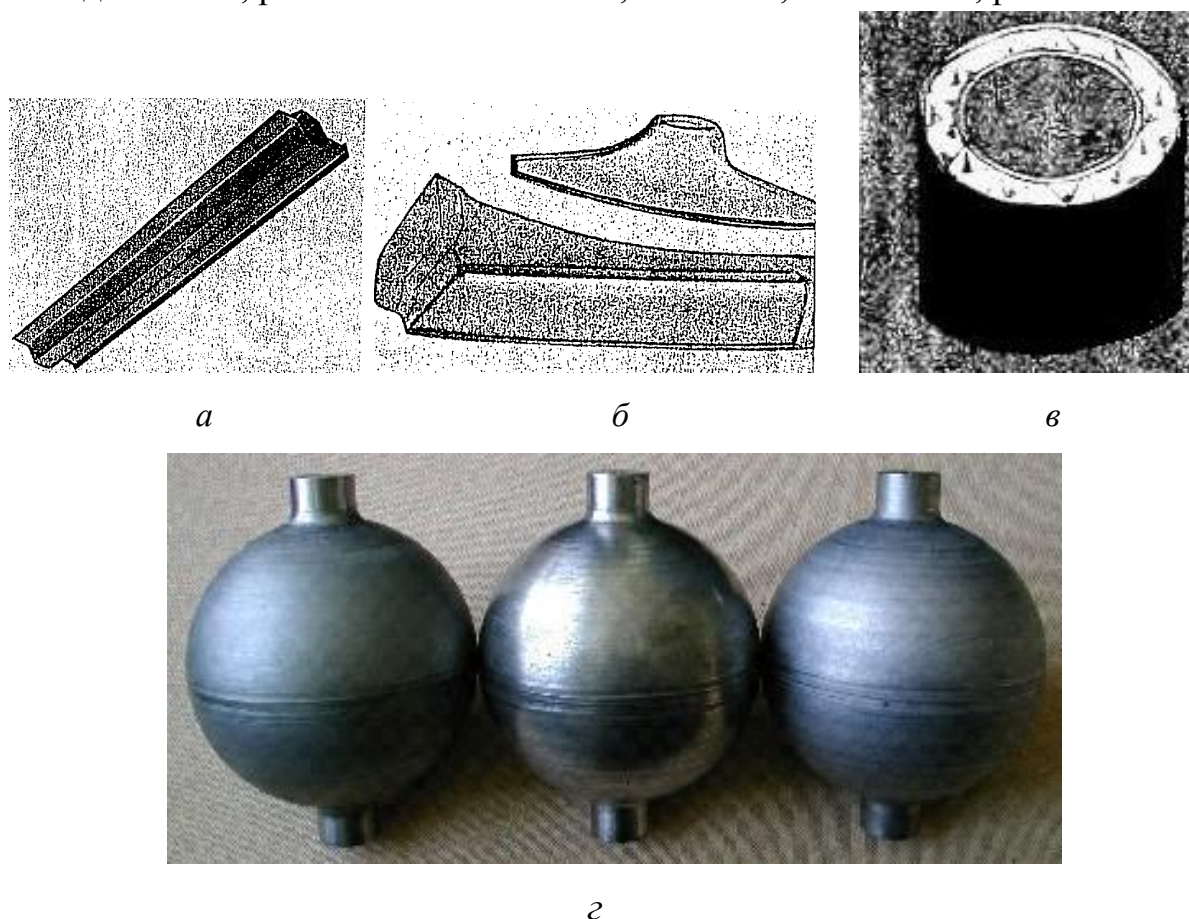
Некоторые виды изделий, полученных технологией сверхпластической формовки в сочетании с диффузионной сваркой:
